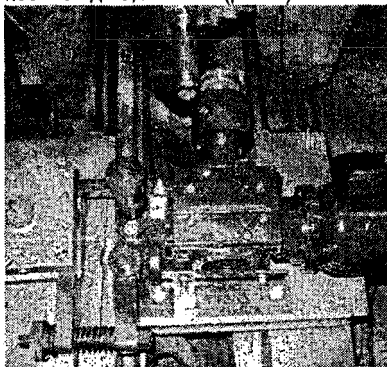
Приспособление для нанесения покрытий трением на токарном станке периферией вращающегося круга
